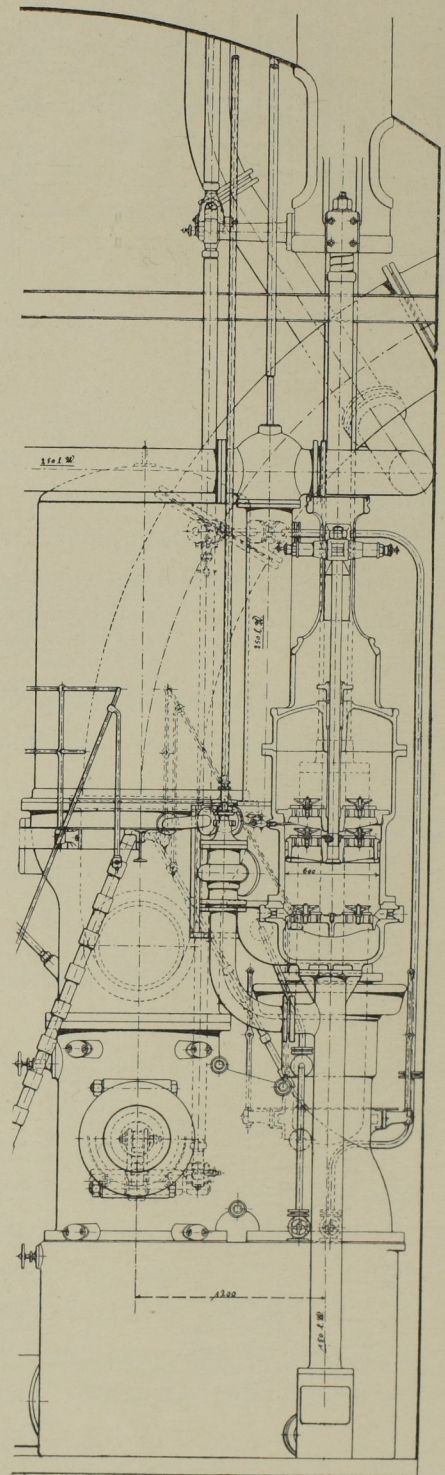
Seitenansicht der Druckpumpe und Luftpumpe.
